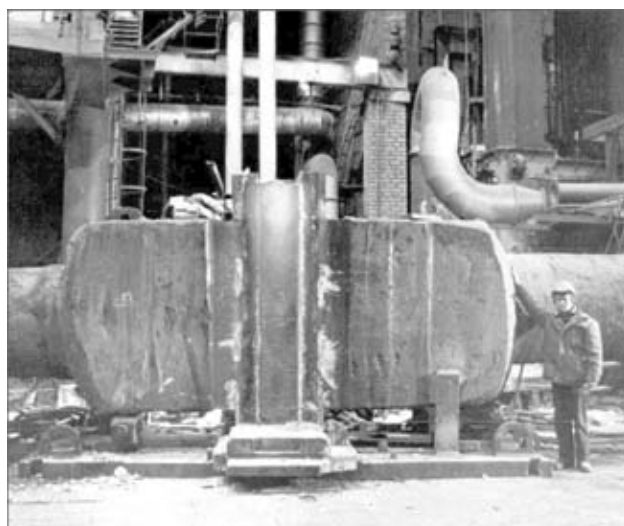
Ковано-сварная заготовка рабочего валка из стали 50ХН массой 103 т для стана ЛП-4500 после сварки способом ЭШС КПМ
